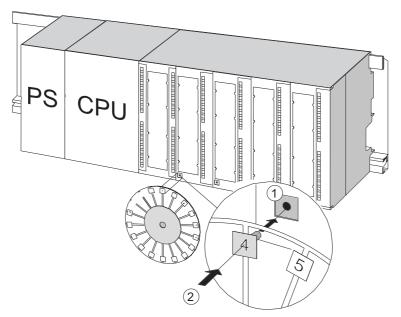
Steckplatznummern auf die Baugruppen stecken
